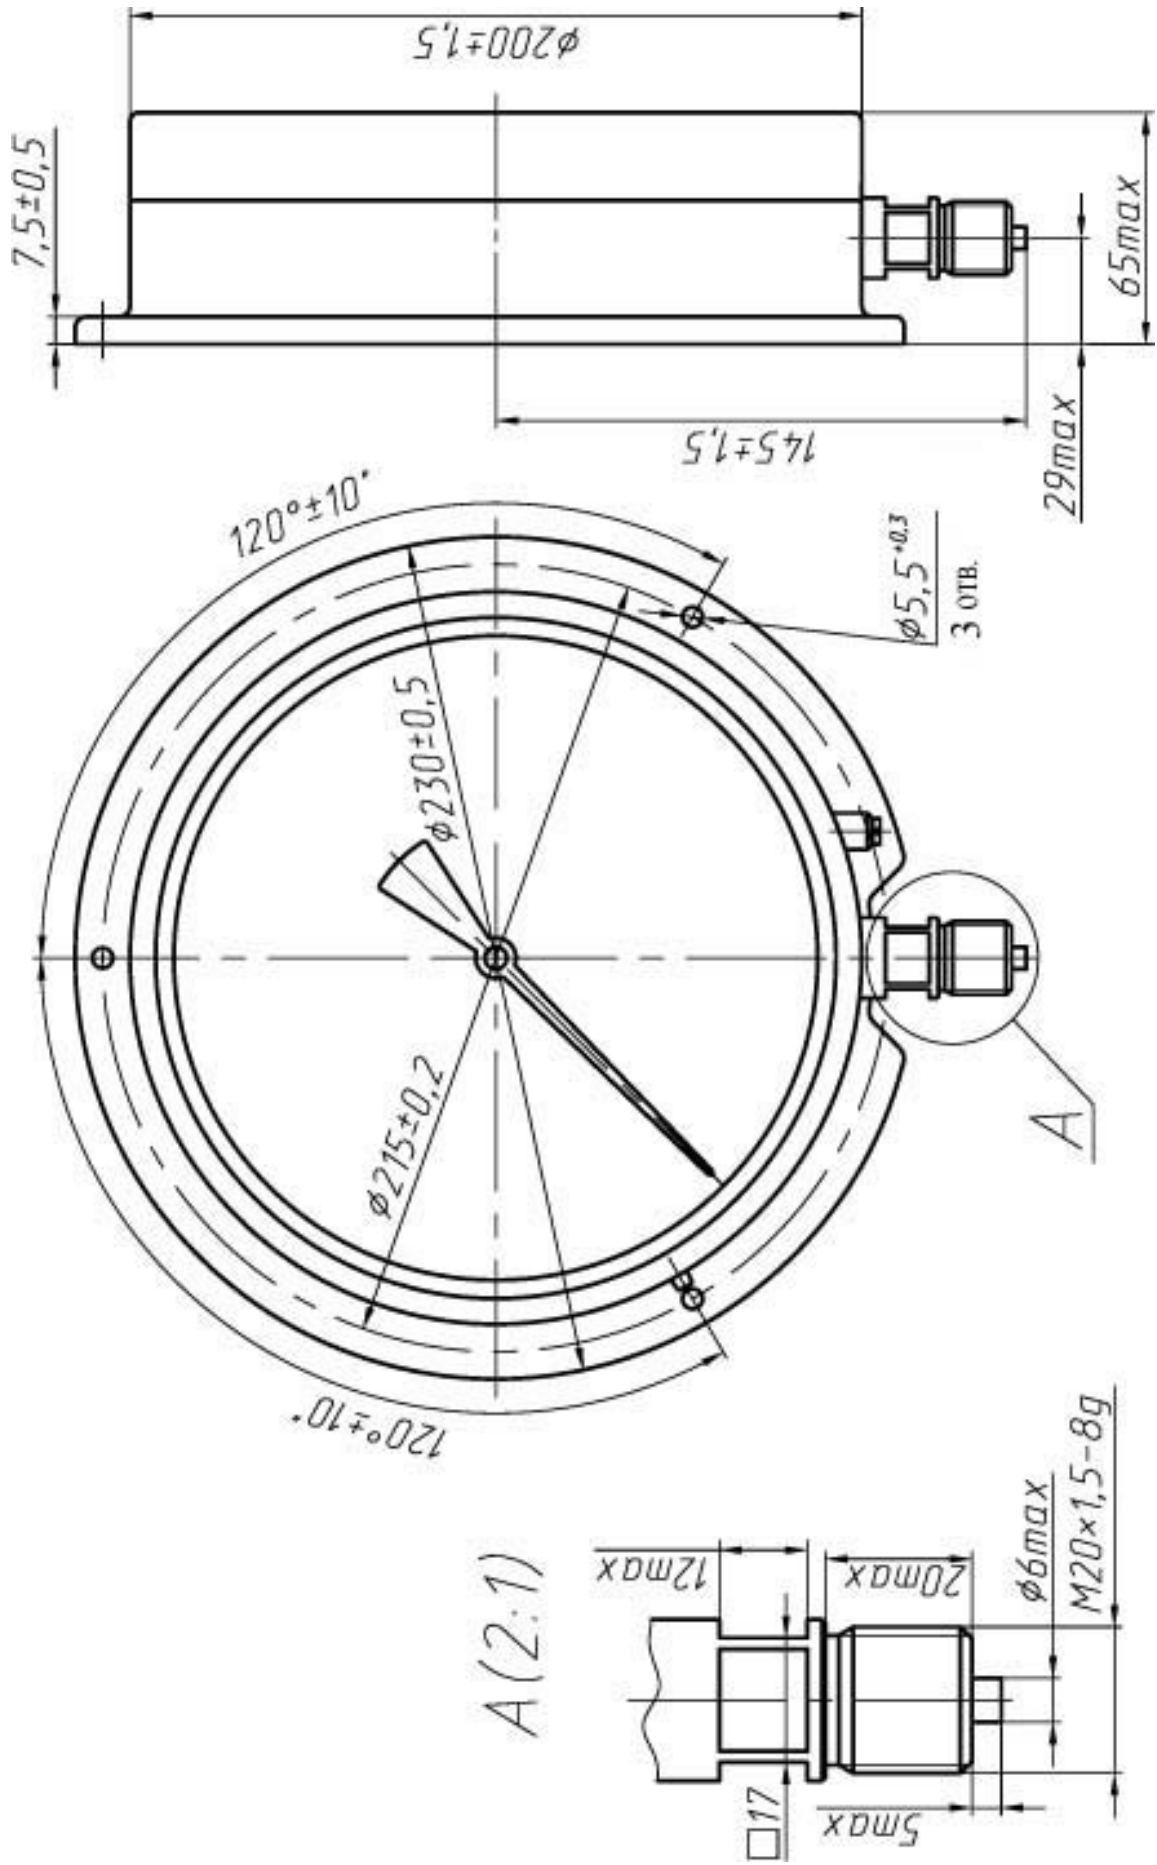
Габаритные и присоединительные размеры глубиномера
